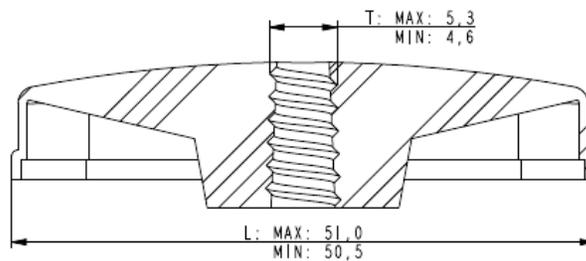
Prueba técnica 2 tolerancia dimensional
